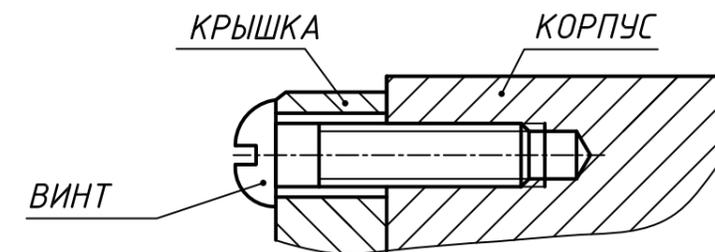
Пример выполнения винтового соединения в разрезе (винт не пересекается, смежные детали крышка и корпус штрихуются в разном направлении)
